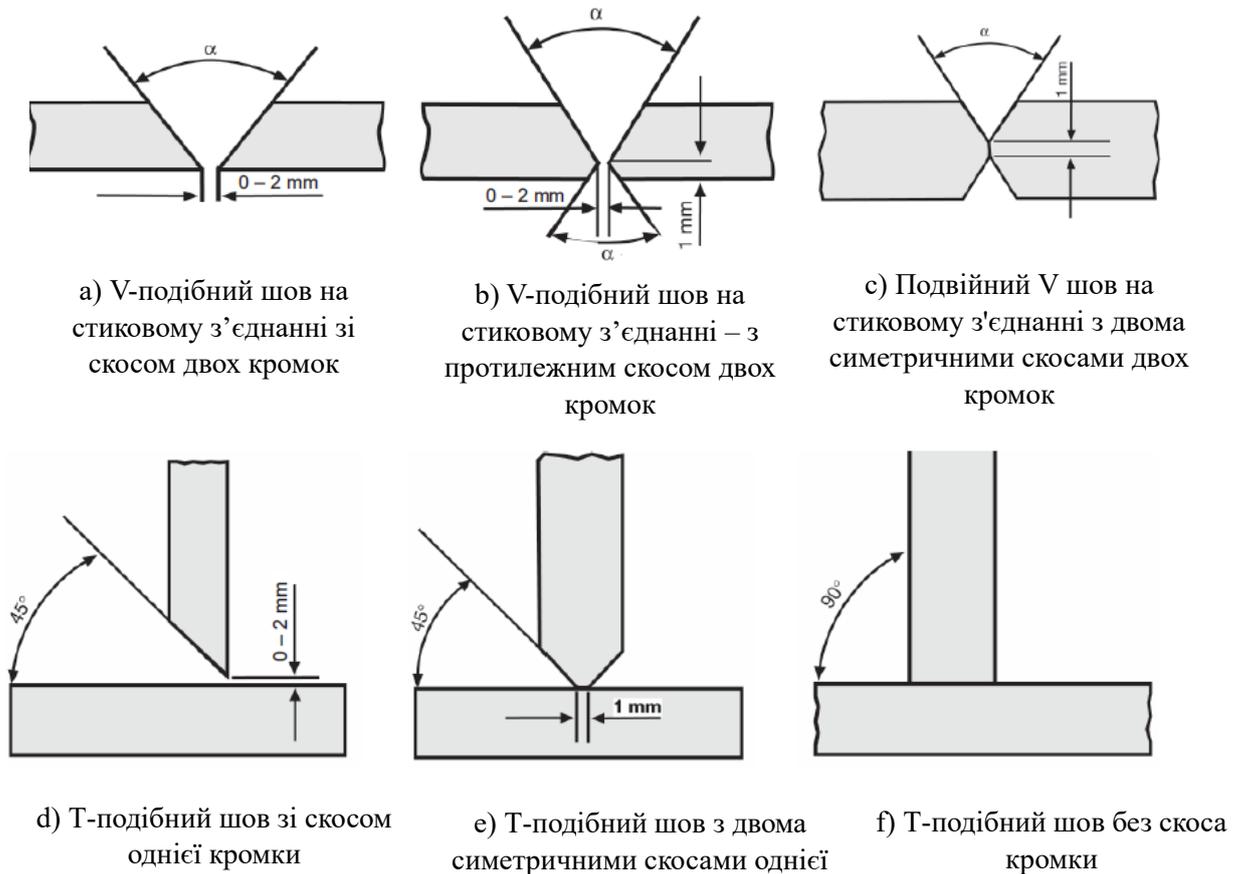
Форми обробки кромки для зварних швів
